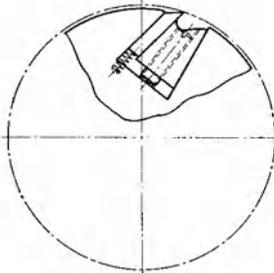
Querschnitt einer geräuscharmen Messerwelle.
